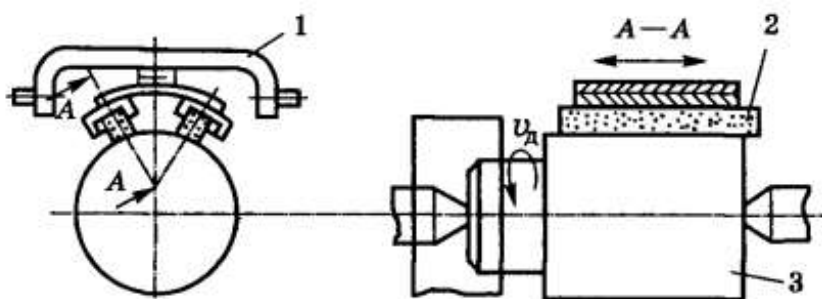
Суперфінішування зовнішньої циліндричної поверхні
